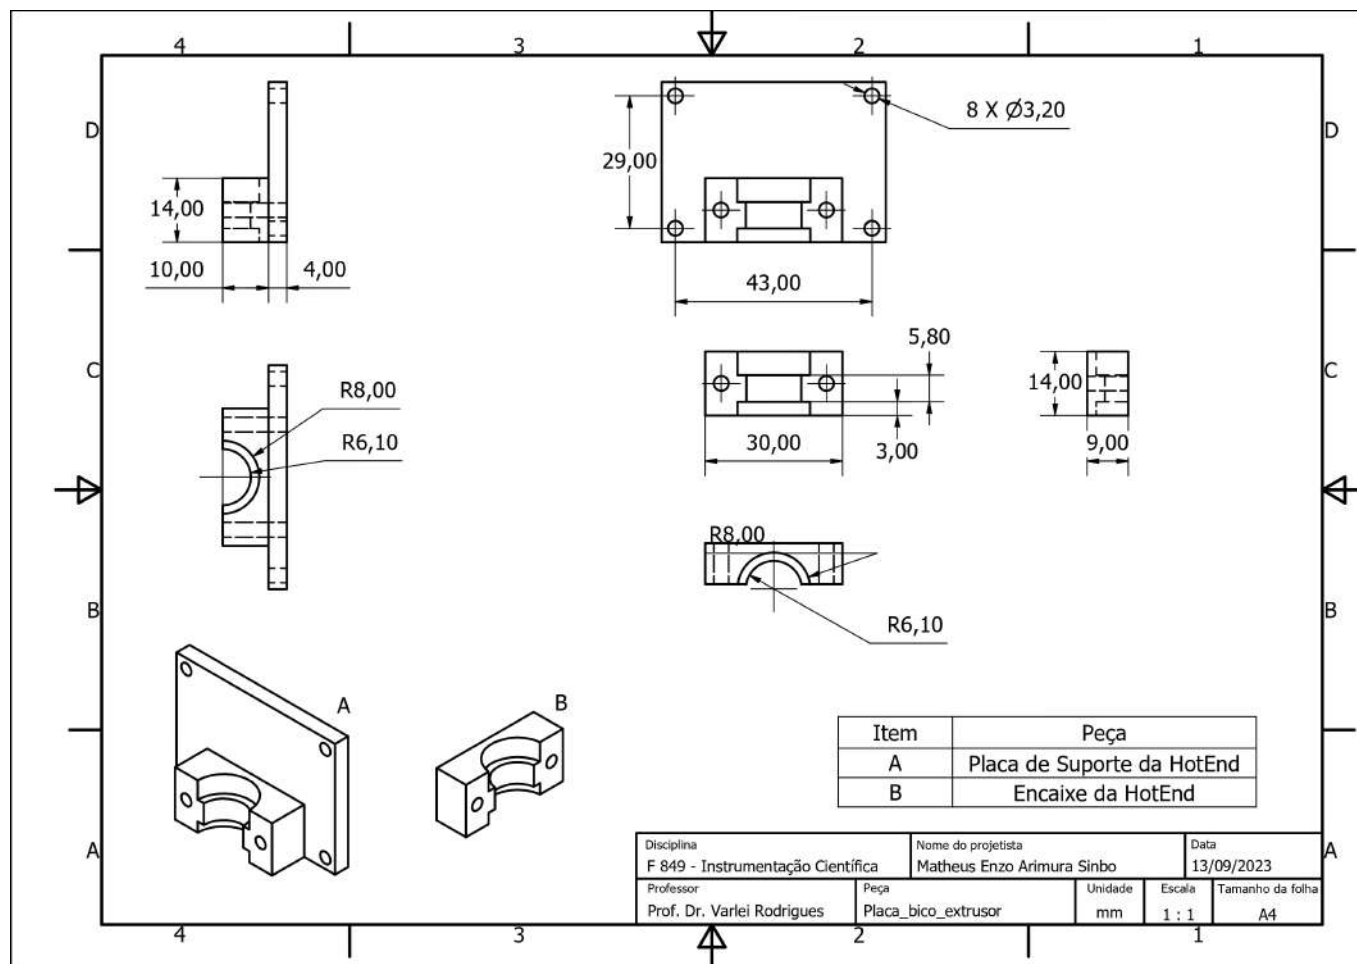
Desenho técnico da placa de suporte do hotend e do encaixe da hotend.
